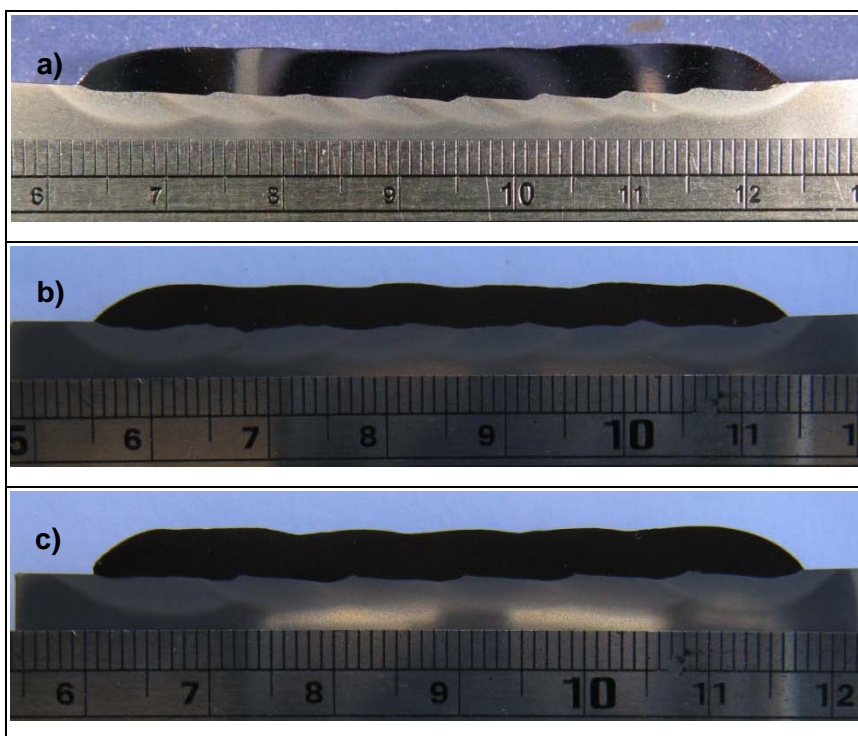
Seção transversal das camadas soldadas com as condições: (a) R1; (b) R2; (c) R3.
